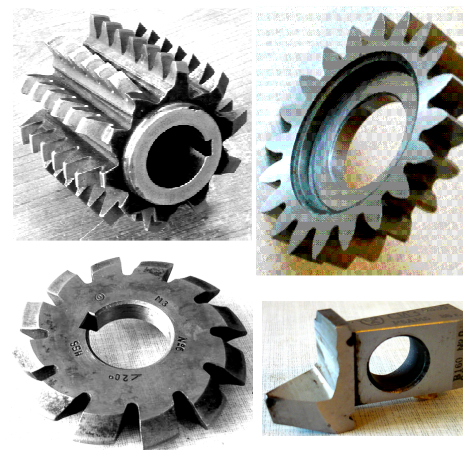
Лезвийные инструменты для нарезания зубчатых колёс:
